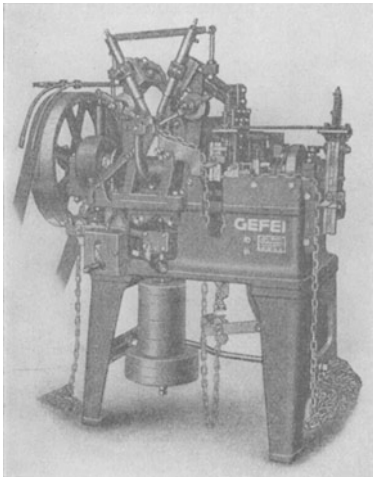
Selbsttätig arbeitende Kettenschweißmaschine.
